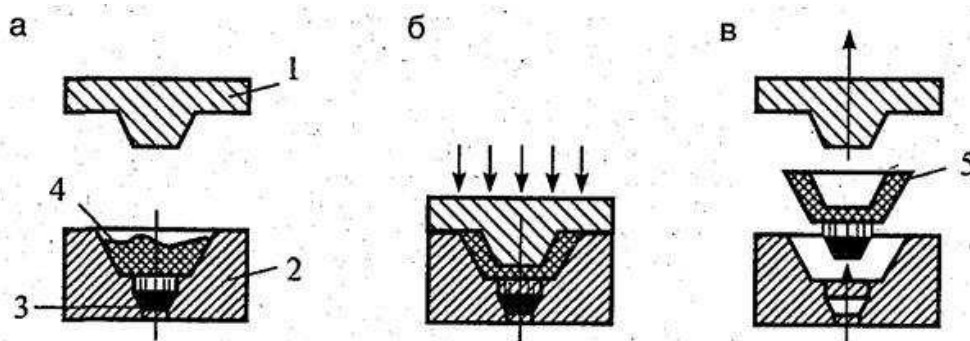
Схема изготовления изделий прессованием [16]: а – загрузка материала в пресс-форму; б – прессование; в – извлечение изделия; 1 – пуансон; 2 – матрица; 3 – выталкиватель; 4 – пресс-материал; 5 – готовое изделие
